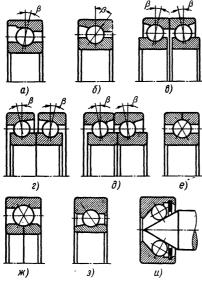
Шарикоподшипники радиальноупорные: a — разборные «магнетные», тип 6000, ГОСТ $831-62^*$; δ — тип 36000, 46000, 66000, ГОСТ $831-62^*$; ϵ — сдвоенные (показаны в свободном состоянии, т. е. до монтажа), тип 236000, 246000, 266000, ГОСТ 832-66; ϵ — то же, тип 336000, 346000, 366000, ГОСТ 832-66; ϵ — то же, тип 436000, 446000, 466000, ГОСТ 832-66; ϵ — с разъемным наружным кольцом, тип 116000, ГОСТ 8995-59; ϵ — с разъемным внутренним кольцом, тип 176000, ГОСТ 8995-59; ϵ — с учоненным внутренним кольцом; ϵ — кольцом; ϵ — миниатюрные
